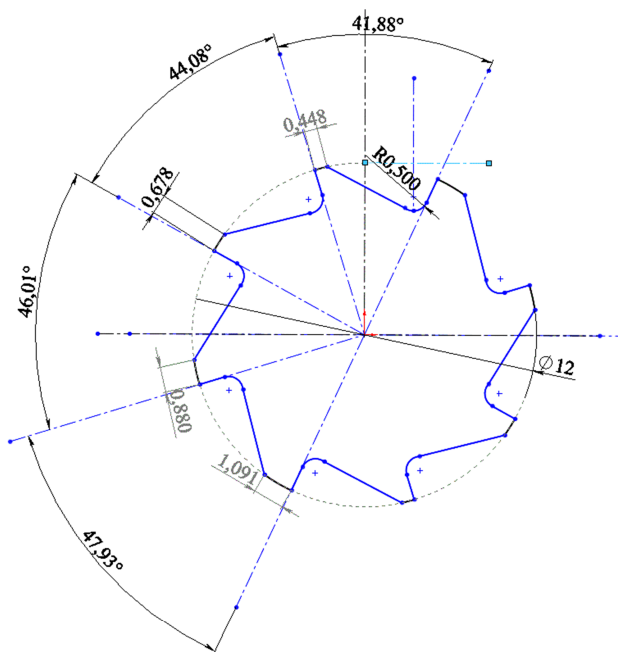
Эскиз профиля развертки с неравномерным окружным шагом:
